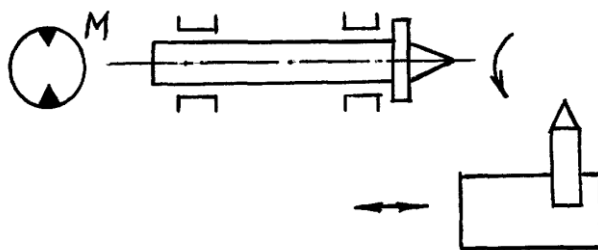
Конструктивная схема работы шпинделя токарного станка
